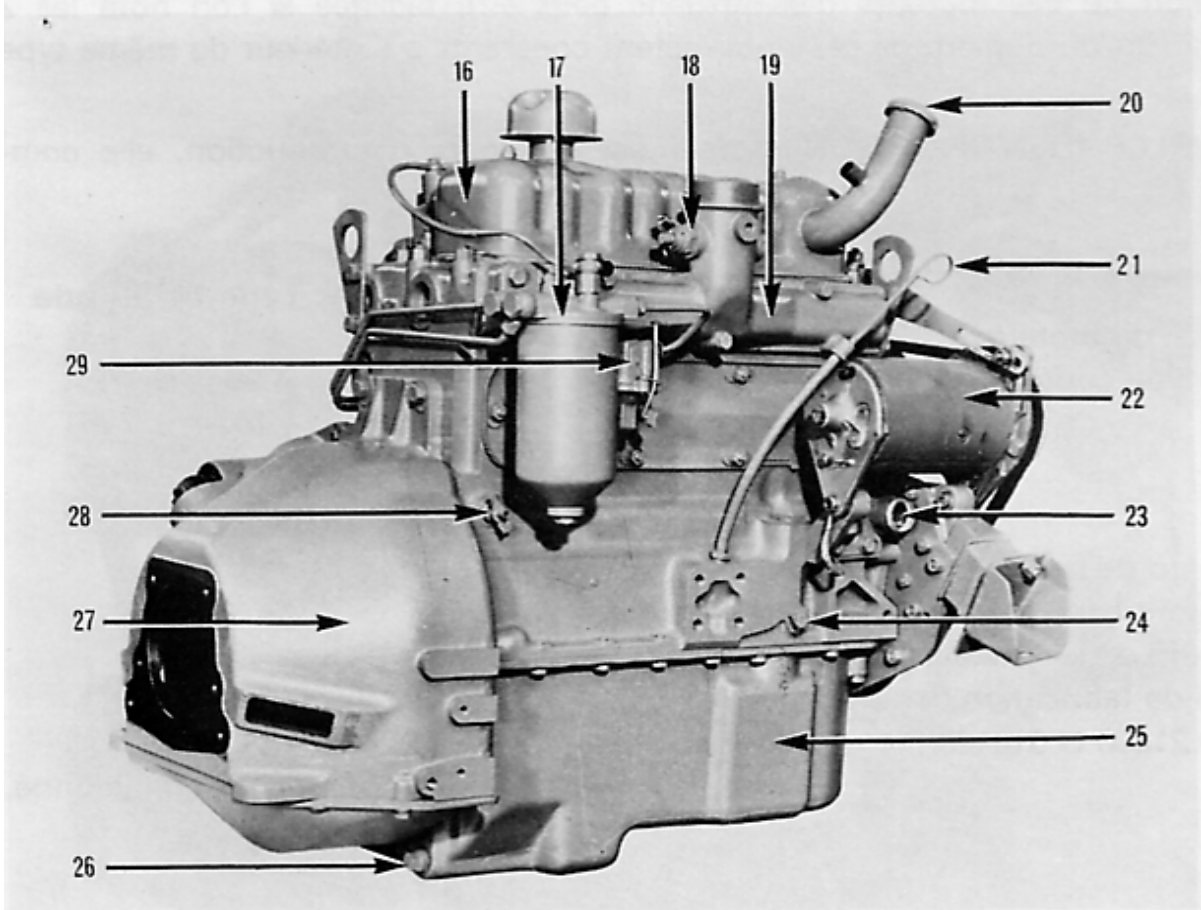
Vue du moteur, côté droit (côté arbre à cames).
